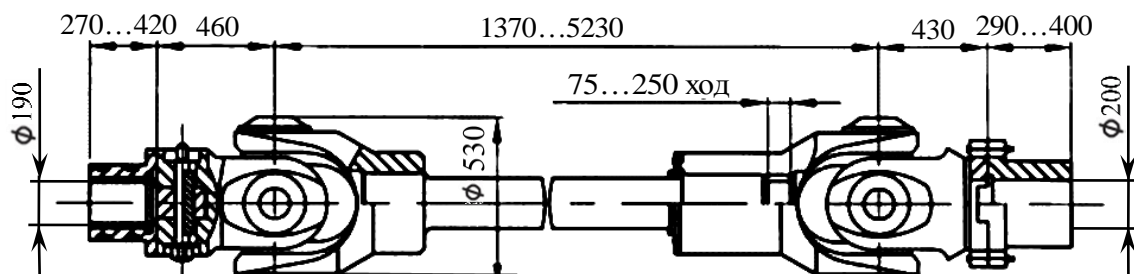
Универсальный шпиндель Ш5-1370 на подшипниках качения
